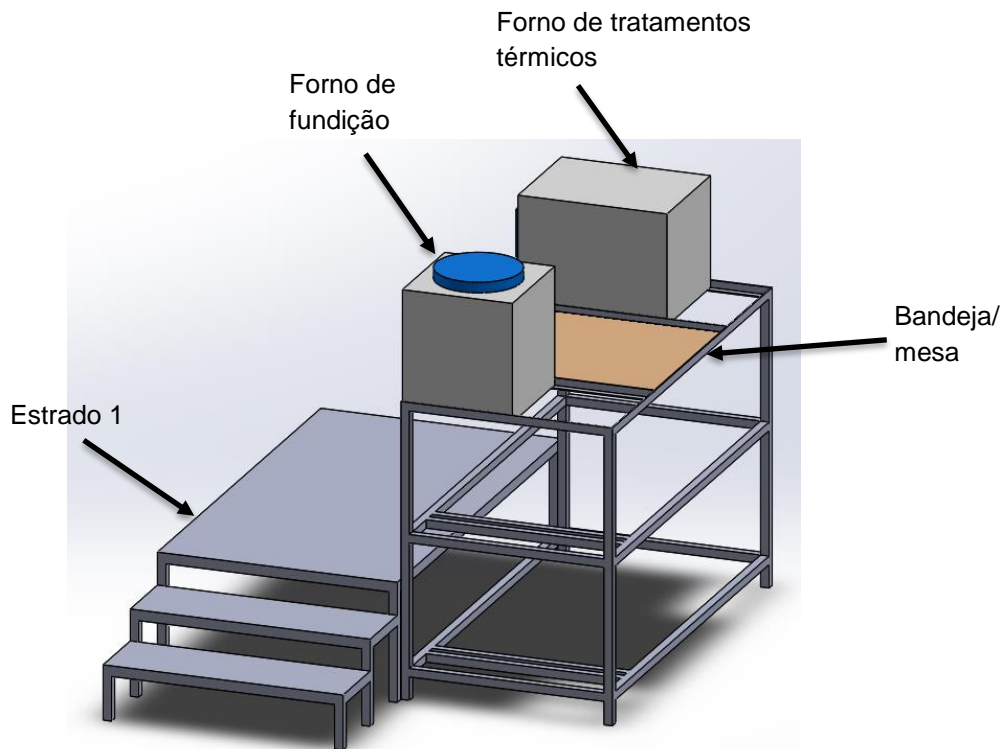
Layout existente no Laboratório de Fundição e Soldadura do DEMI, desenhado em *SolidWorks*.
